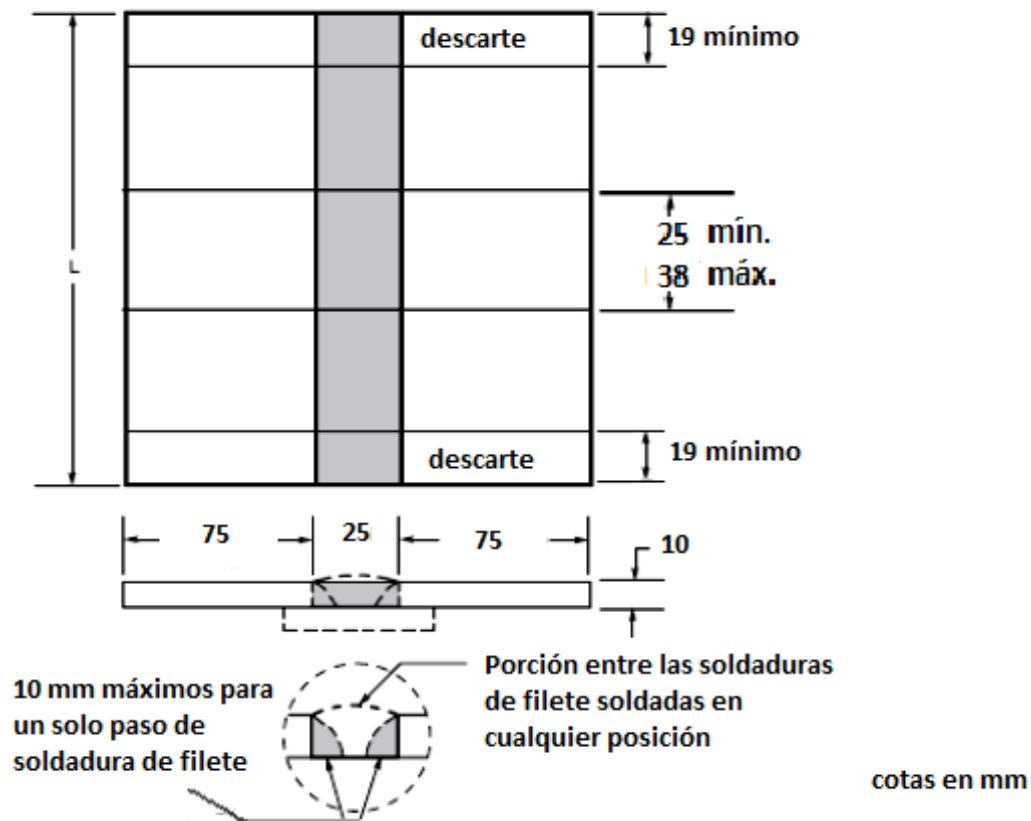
Probeta para curvatura de raíz de soldadura de filete [3].
